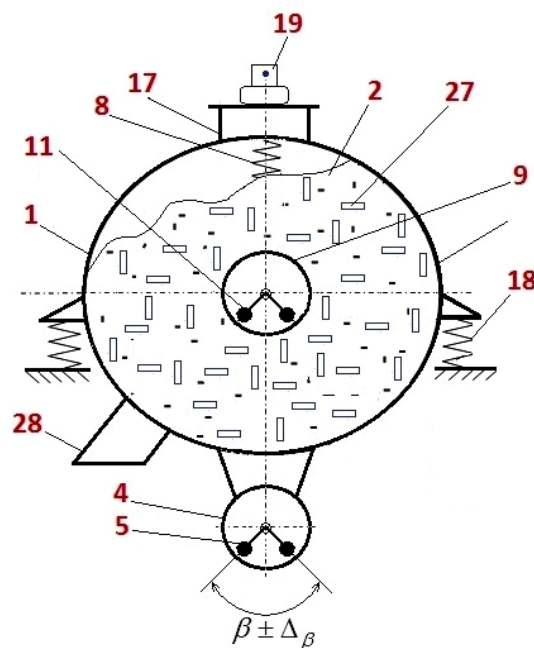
Структурна схема розташування керованого синхронного дебалансного віброприводу контейнера та активатора, у пристрої для адаптивної віброабразивної обробки деталей
